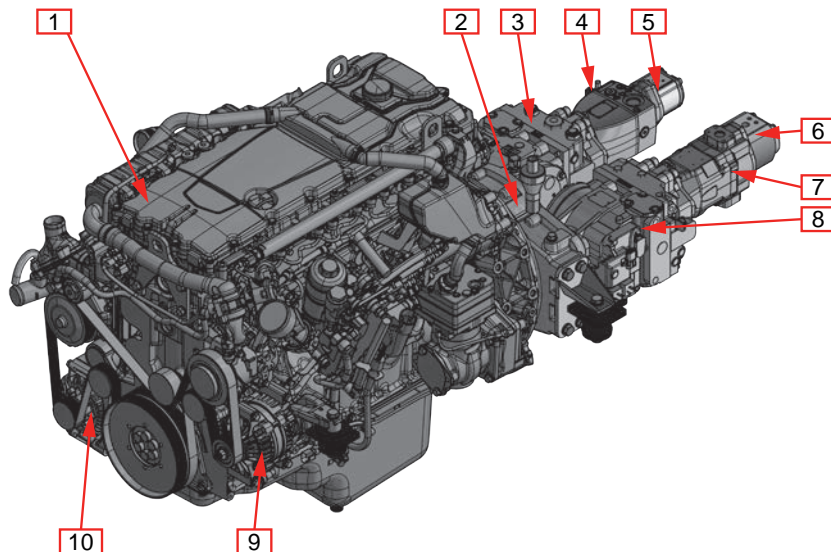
Motor und Hydraulikpumpen DT 2400H
